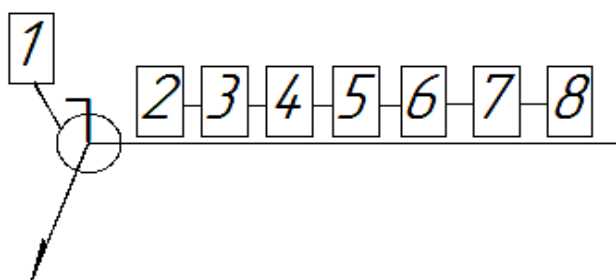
Условное обозначение шва сварного соединения
